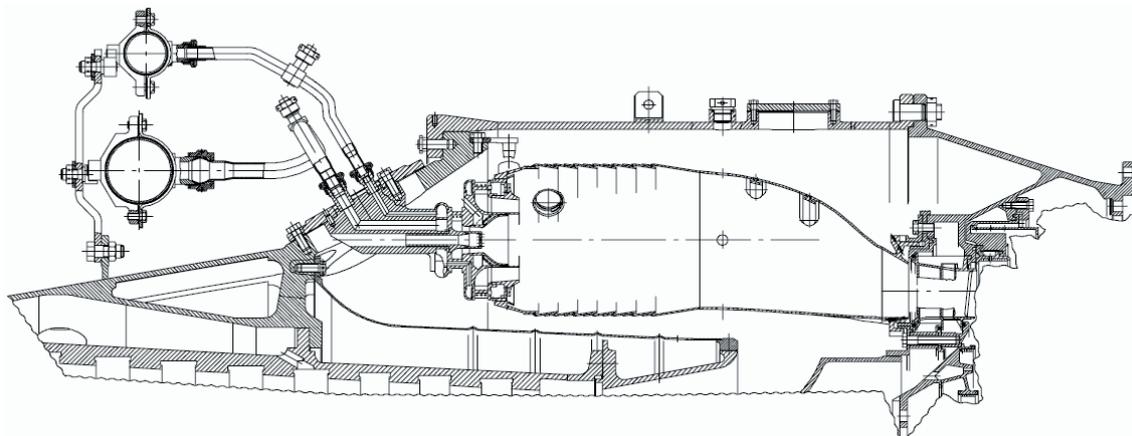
Конструктивная схема камеры сгорания газотурбинного двигателя ДН80
